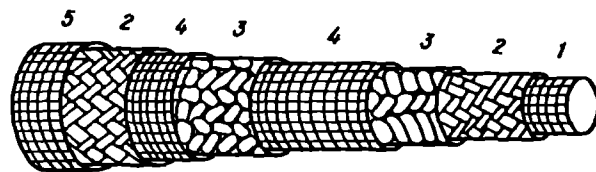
Конструкция рукава высокого давления с металлической оплеткой:
